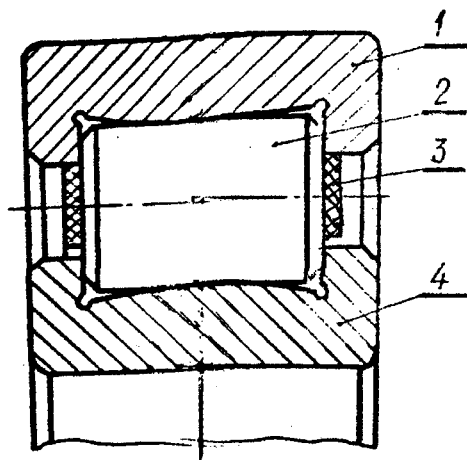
Роликоподшипник с цилиндрическими роликами и оптимизированным профилем дорожек качения: 1 - наружное кольцо; 2 - цилиндрический ролик; 3 - сепаратор; 4 - внутреннее кольцо
